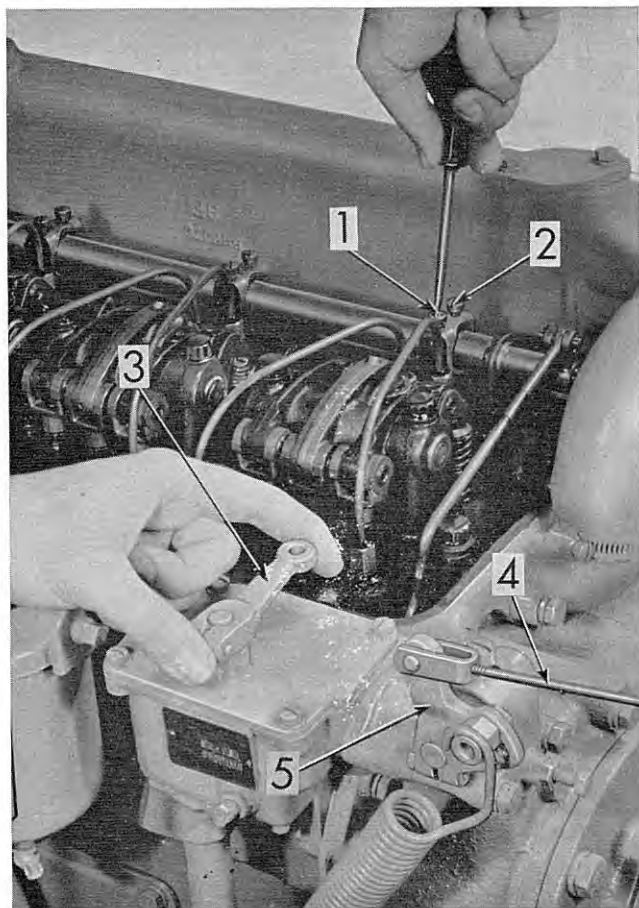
Réglage du levier arrière de commande d'injecteur
